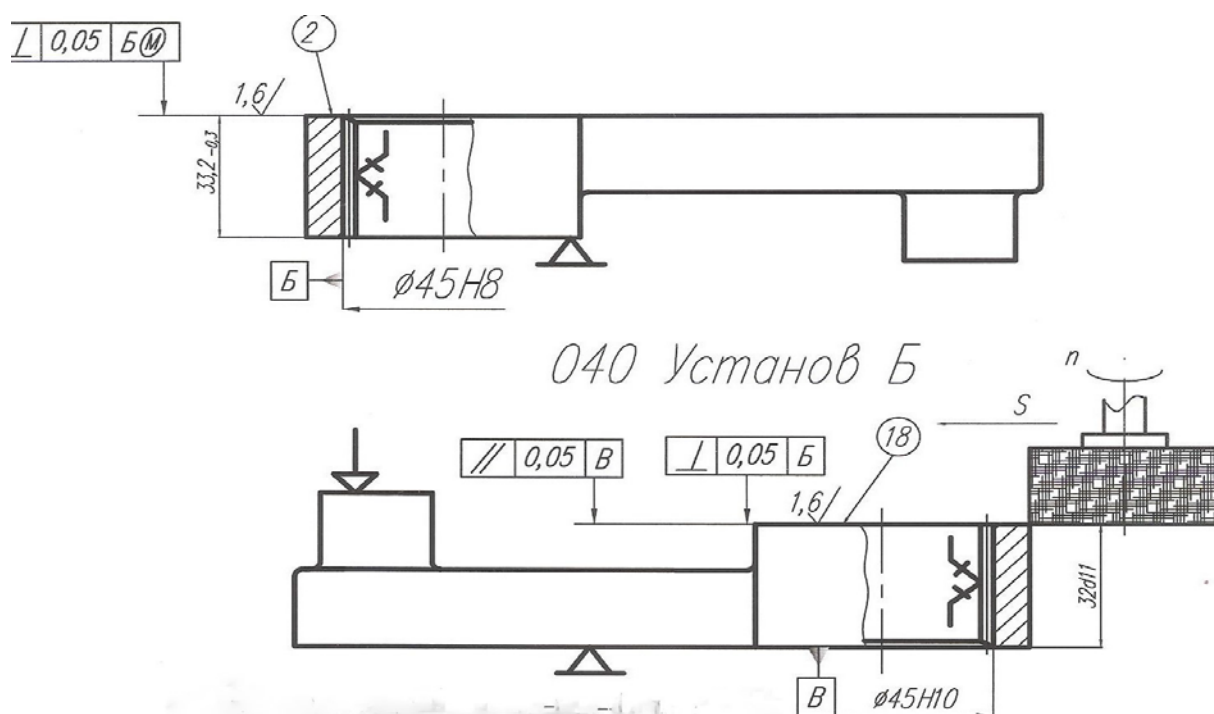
Схема базирования заготовки на операции 025 установ Б
